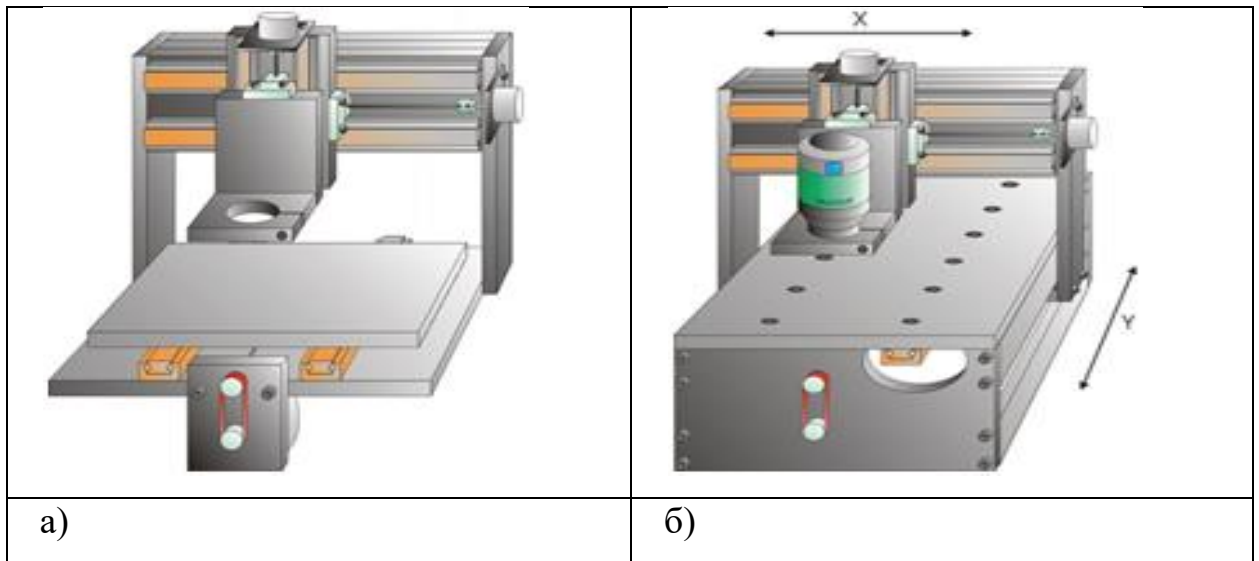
Схема порталних систем, де: а)- рухомий стіл для розміщення деталі; б) – рухомий портал
